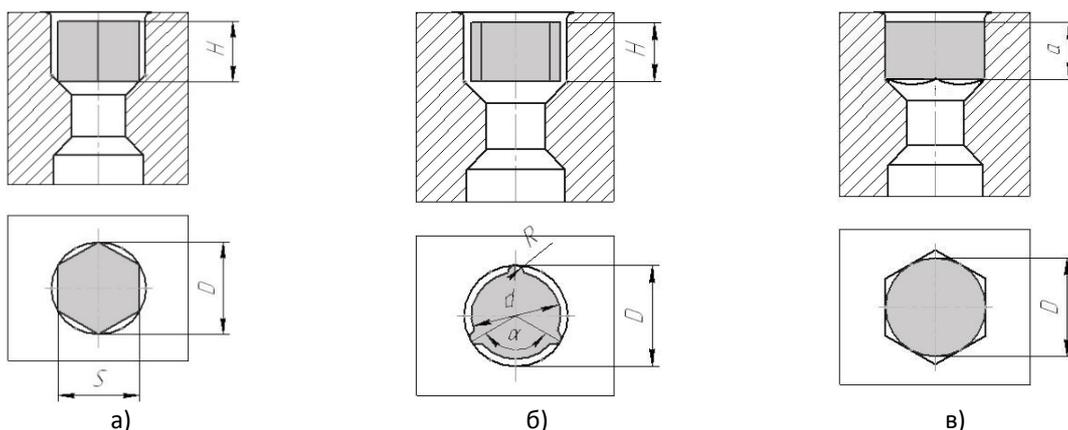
Схемы установки заготовок в матрицу перед выдавливанием: а) заготовка с ребрами; б) шестигранная в круглой полости; в) круглая в шестигранной полости.
